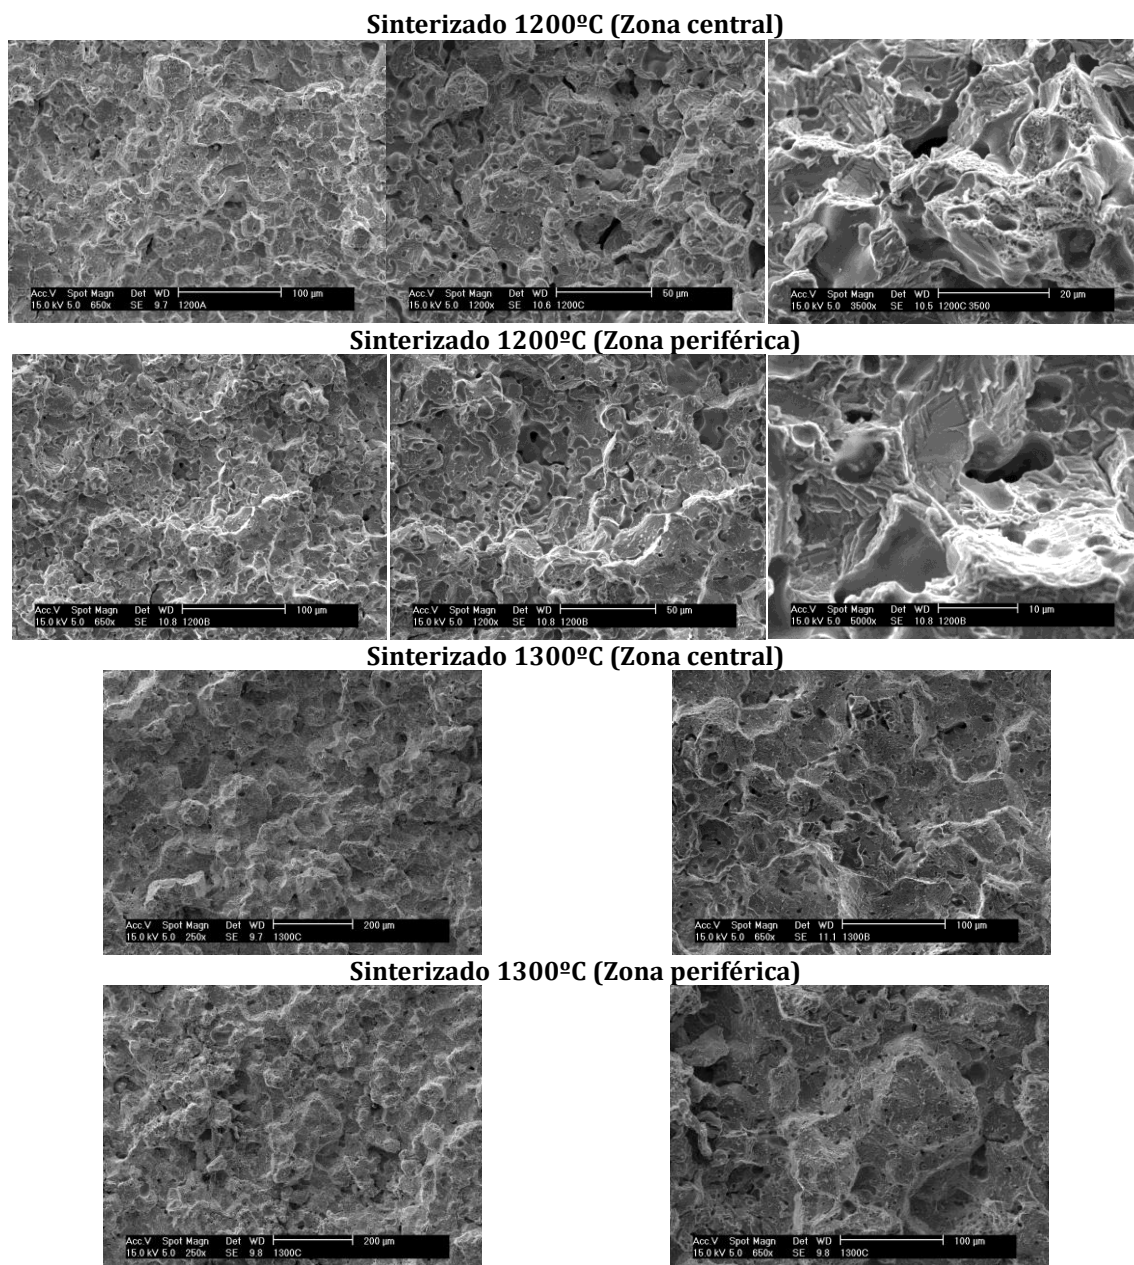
Superficie de fractura de probetas de tracción. (De izquierda a derecha de menor a mayor aumento)
